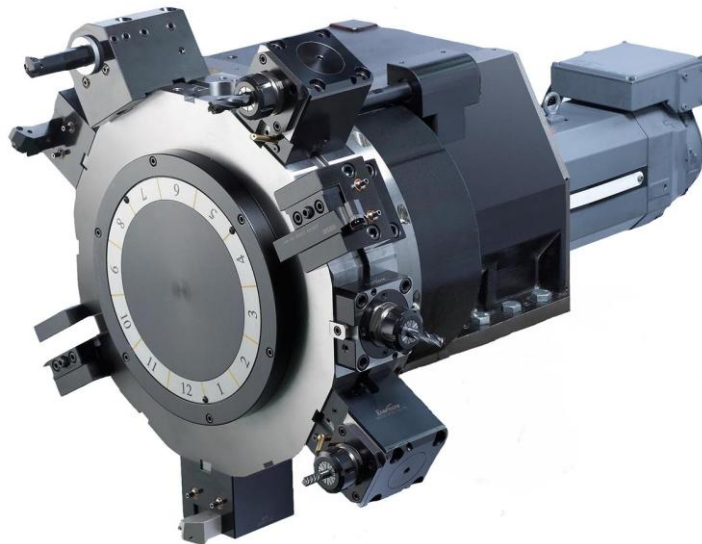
Револьверная головка с неподвижными и вращающимися инструментами
